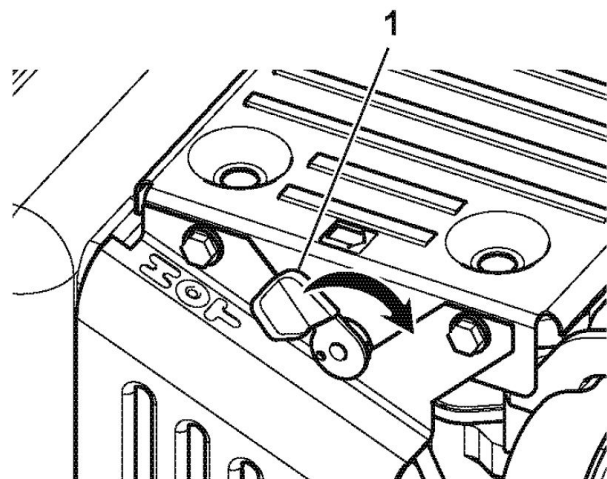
Motor mit manueller Dekompressionsvorrichtung
